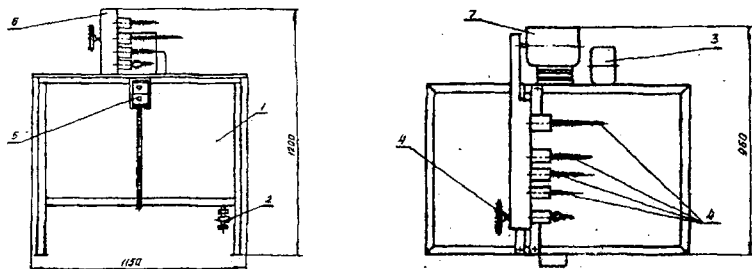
Установка для мойки и чистки доильных аппаратов:
